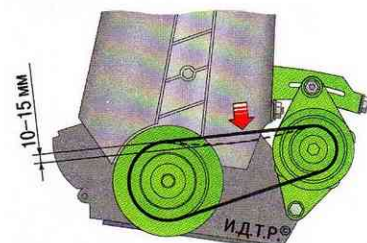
Схема проверки натяжения ремня привода генератора
